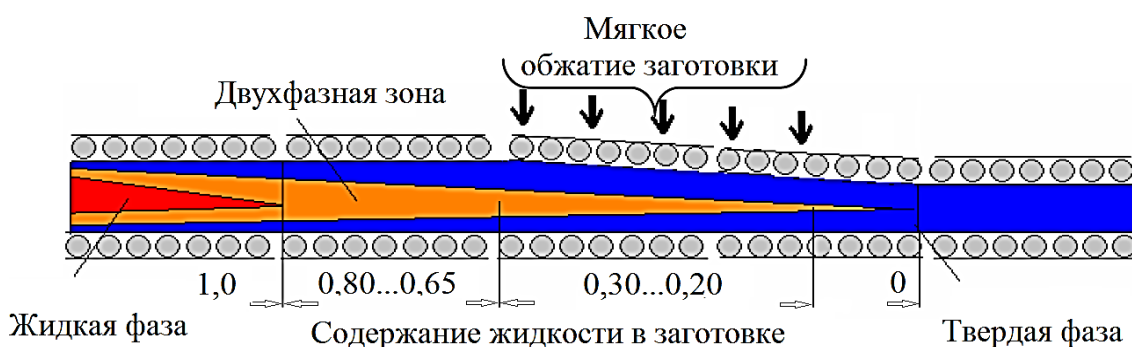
Схема мягкого обжатия слябовой непрерывнолитой заготовки в процессе разливки
